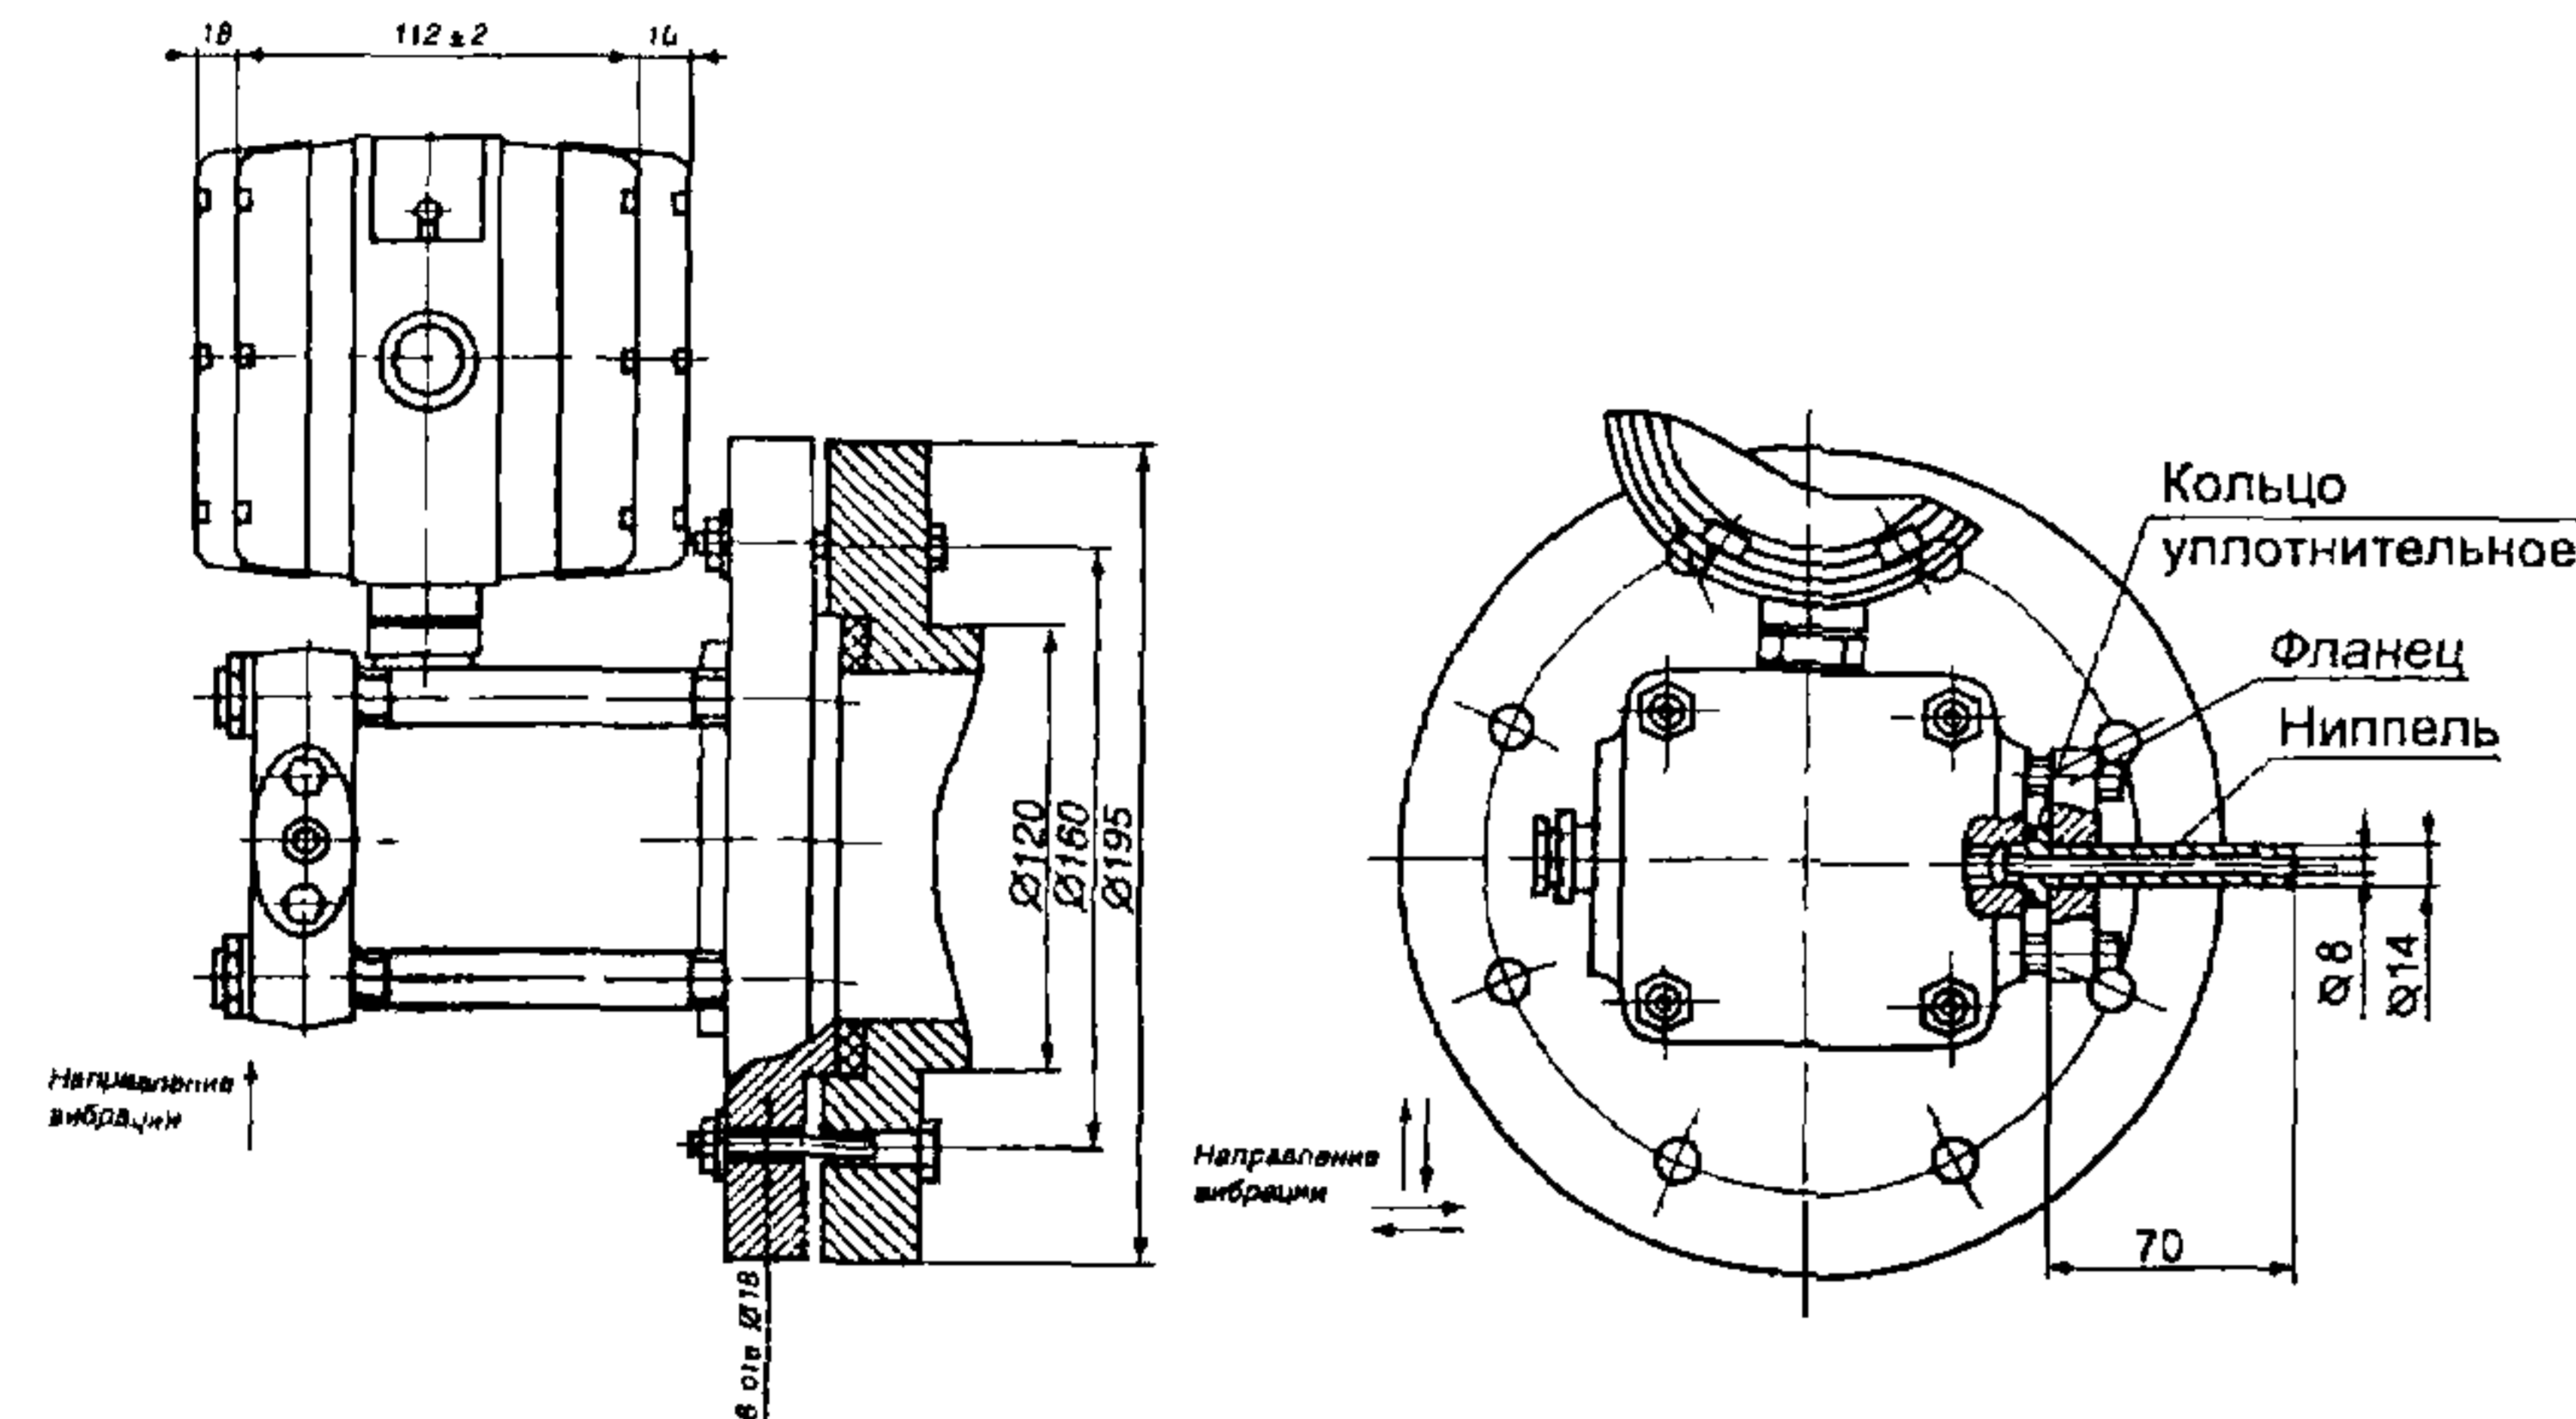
Преобразователь с установленными ниппелями под накидные гайки M20x1,5, остальное см. рис.12
